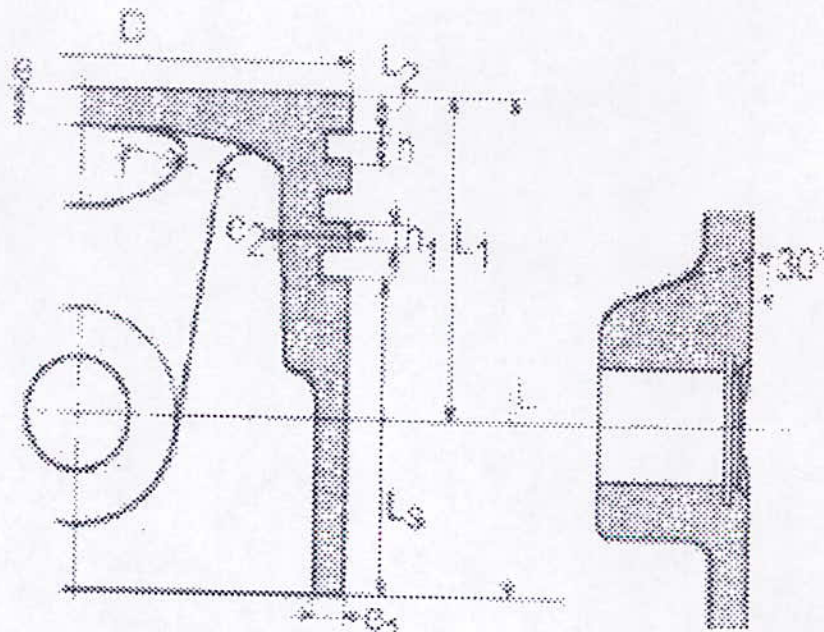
Dimensions du piston pour moteur à allumage commandé ou moteur DIESEL [7].
